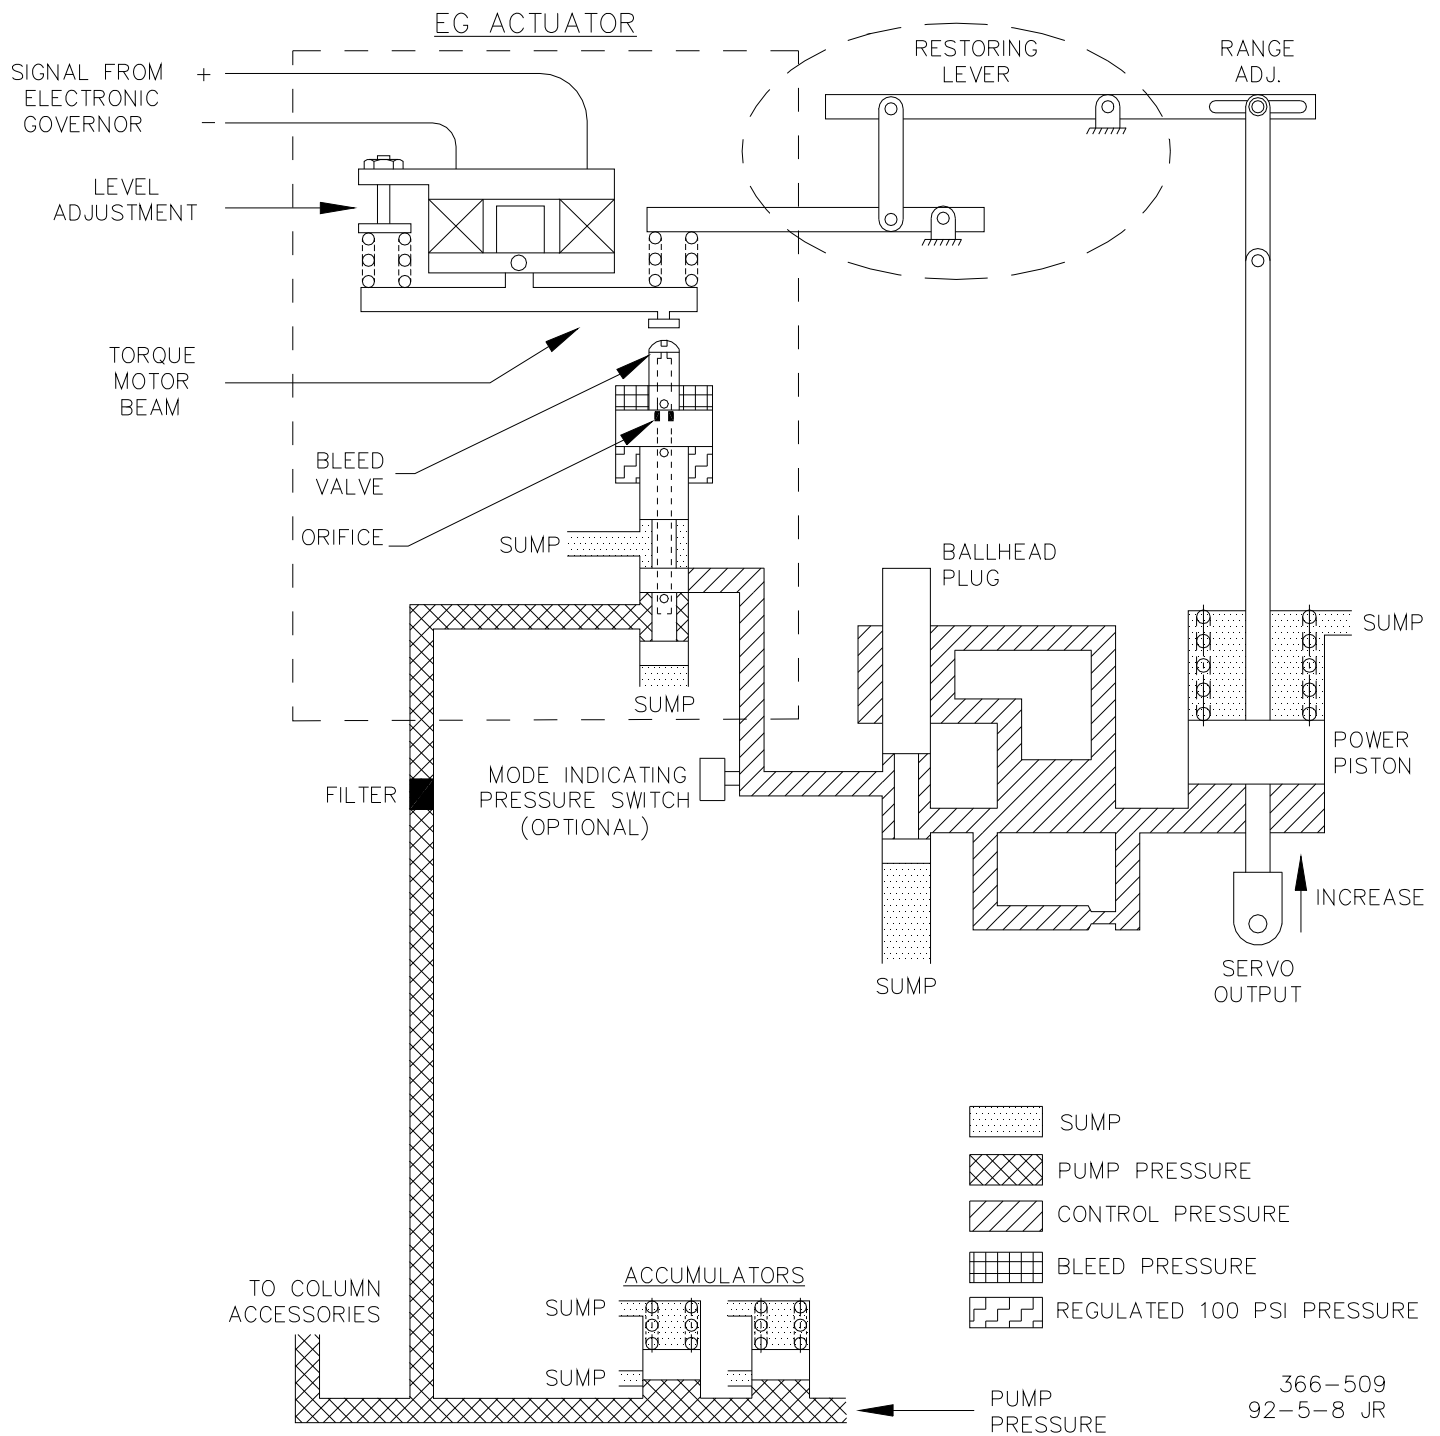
Схематичное изображение привода EG, без резервирования шаровой головки
